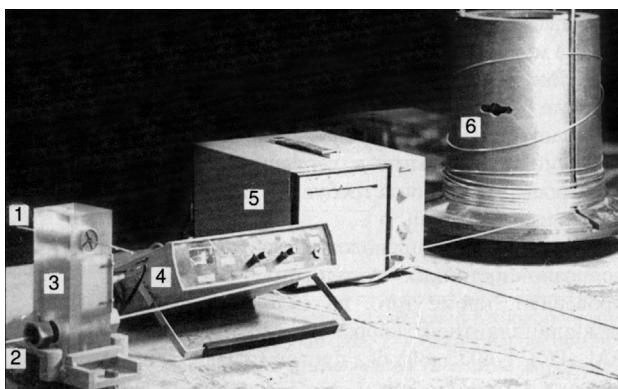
Прибор ПДС-2М контроля качества сварочной проволоки: 1 – эталонный образец проволоки; 2 – контролируемая проволока; 3 – датчик; 4 – электронный блок; 5 – самописец; 6 – намоточное устройство
